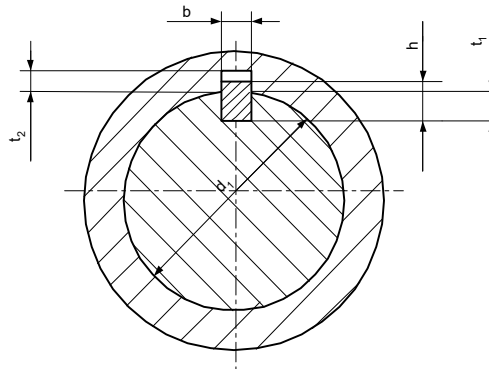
Розрахункова схема шпонкового з'єднання
